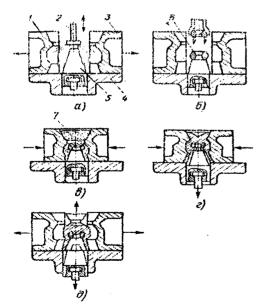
Схема изготовления отливки в металлической форме (кокиле):
